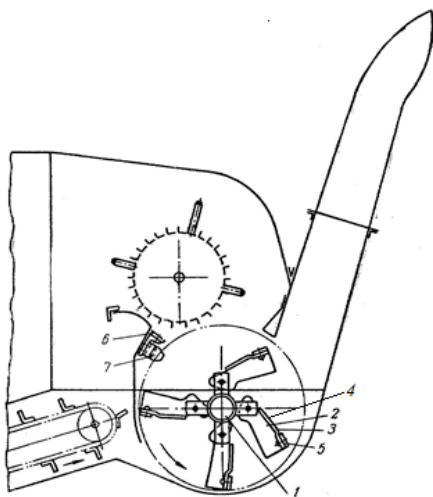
Измельчитель соломы и подобных материалов: 1 — вал; 2 — кронштейны; 3 — лопатка; 4 — плоский участок; 5 — режущая пластина; 6 — противорежущие элементы; 7 — ножи
